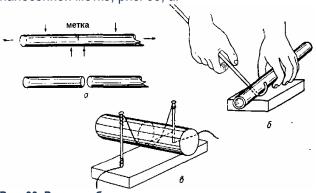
Резка трубок: а —холодный разрез (на излом); б—при помощи раскаленного крючка; в —при помощи проволоки, накаливаемой током.
